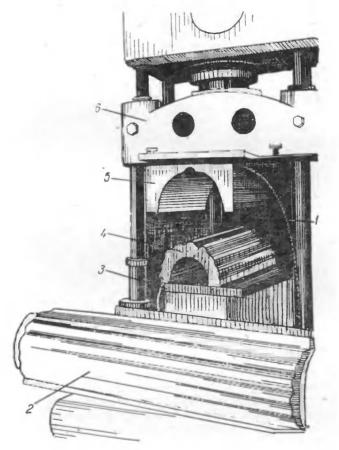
Установка пневмокамеры на четырехколонном прессе верхнего давления:
